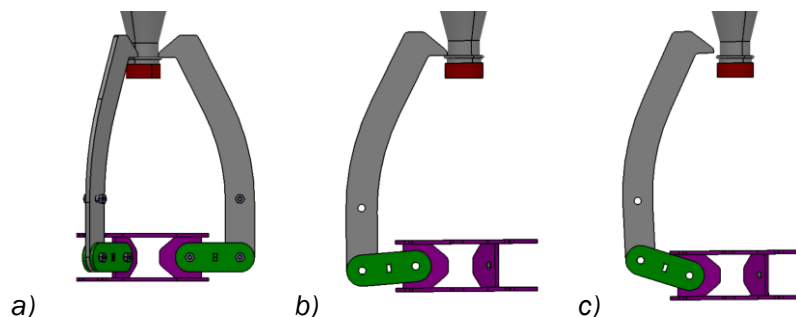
Posiciones de trabajo del mecanismo principal. a) Posición cero; b) Posición I; c) Posición III.
